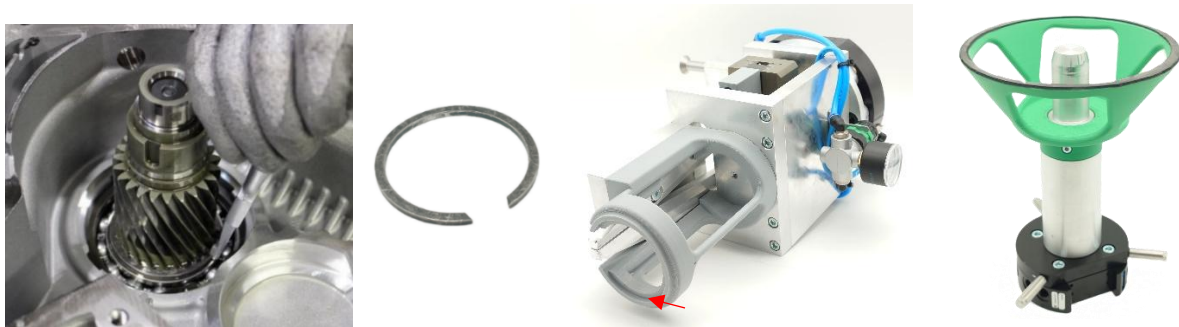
Sicherungsring auf der Rotorwelle (links) und einzeln dargestellt (Mitte links). Mitte rechts: Werkzeug zum Lösen und Entfernen des Sicherungsringes, welcher in die Nut (roter Pfeil), eingepresst und abgeführt wird. Rechts: Hilfswerkzeug zum Drehen des Rotors, um die Position der Öffnung des Sicherungsringes in eine vorher definierte Lage zu realisieren.
